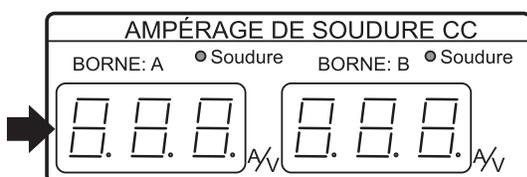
Codes d'erreur des appareils de mesure de la soudure en CC
